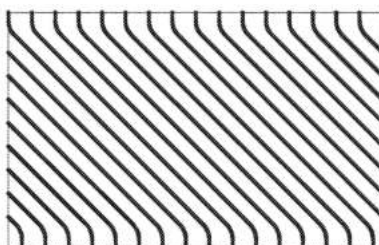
Фрагмент розгортки стрічки дискового сепаратора згідно з пат. № CN205095810U
